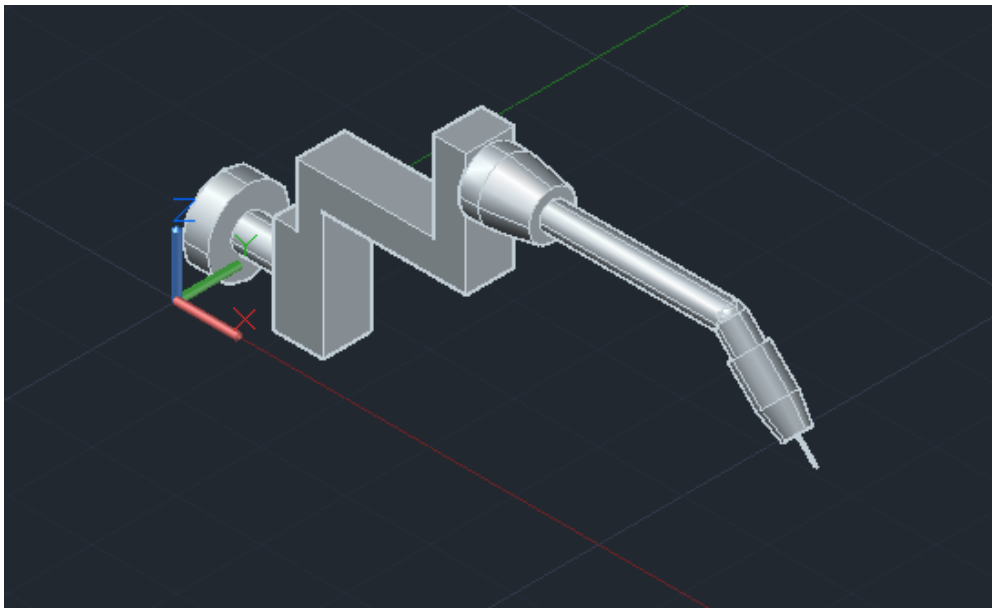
Pistola de soldadura Dinse Dix Metz 594 (45°).
